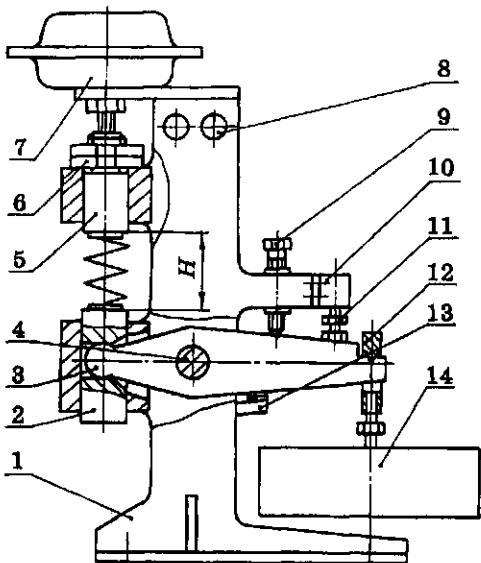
Стенд для контроля жесткости пружин: 1 — корпус; 2, 5 — скалки; 3 — рычаг; 4 — ось; 6 — гайки регулировочные; 7 — пневмокамера; 8 — световой индикатор; 9 и 11 — болты регулировочные; 10 — конечный выключатель; 12 — призма; 13 — упор; 14 — груз
